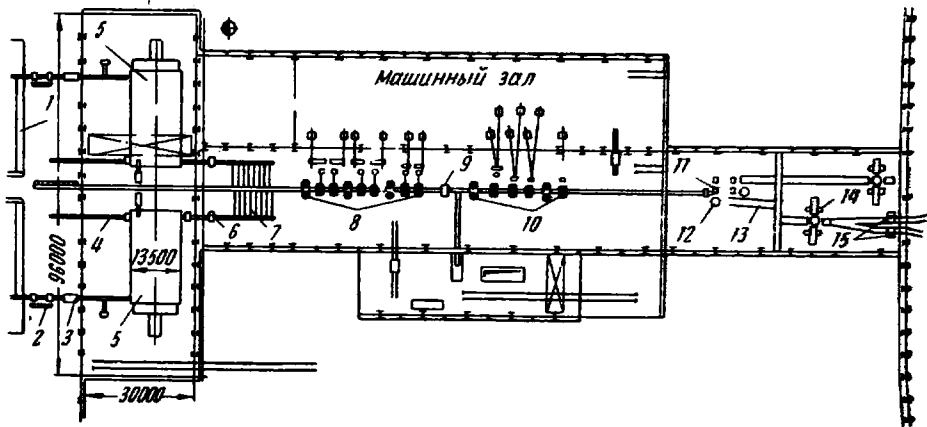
Схема расположения оборудования непрерывного штрипового стана: 1 — загрузочные решетки; 2 — кангователи; 3 — вталкиватели; 4 — выталкиватели; 5 — печи; 6 — ножницы; 7 — шлепперы; 8 — черновая непрерывная группа клетей; 9 — аварийные летучие ножницы; 10 — чистовая непрерывная группа клетей; 11 — моталки; 12 — съемники бунтов; 13 — транспортеры бунтов; 14 — бунтовязальные машины; 15 — пакетирующие бунтов
